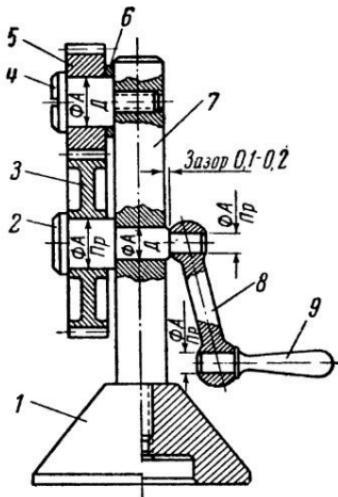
Модель цилиндрической зубчатой передачи (схема соединения деталей).
